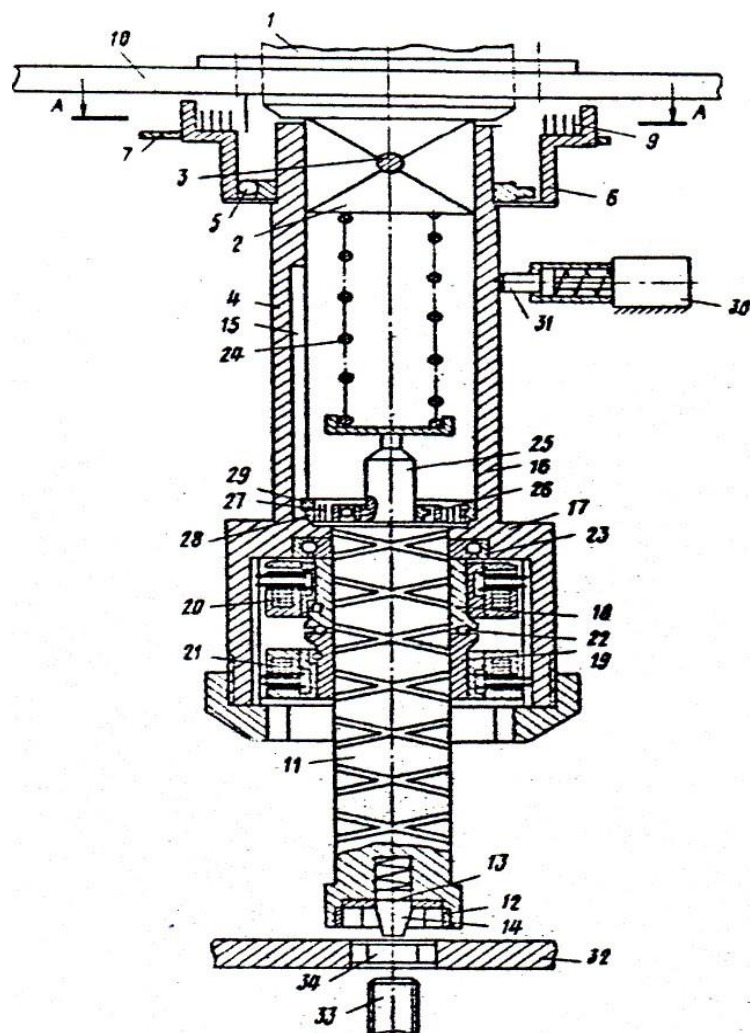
Пристрій для орієнтування, наживлення і нагвинчування кріпильних деталей.
